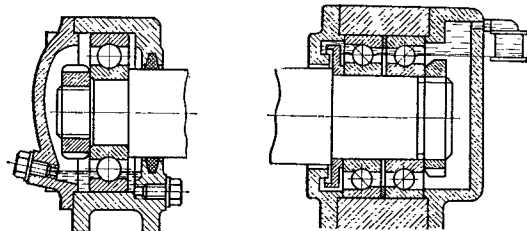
Сливное отверстие в крышке корпуса тихоходного подшипника
